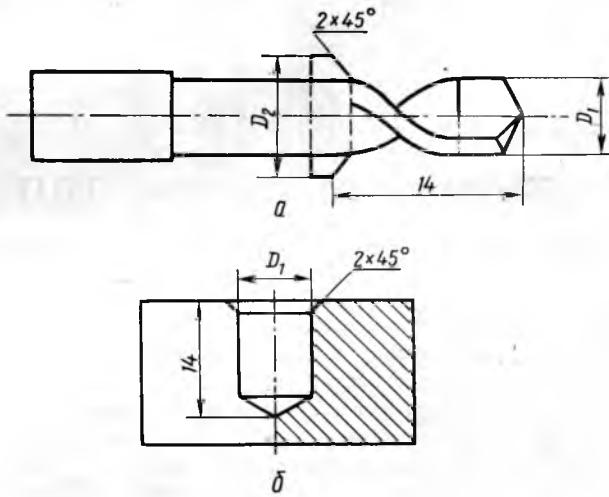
Комбинированное сверло (а) и шаблон (б) для его заточки и изготовления
